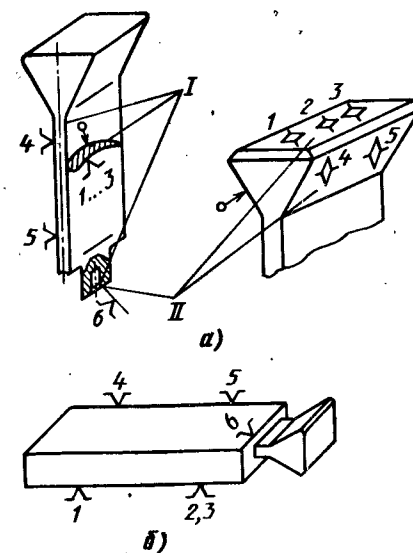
Технологические базы для обработки рабочих лопаток компрессора:
